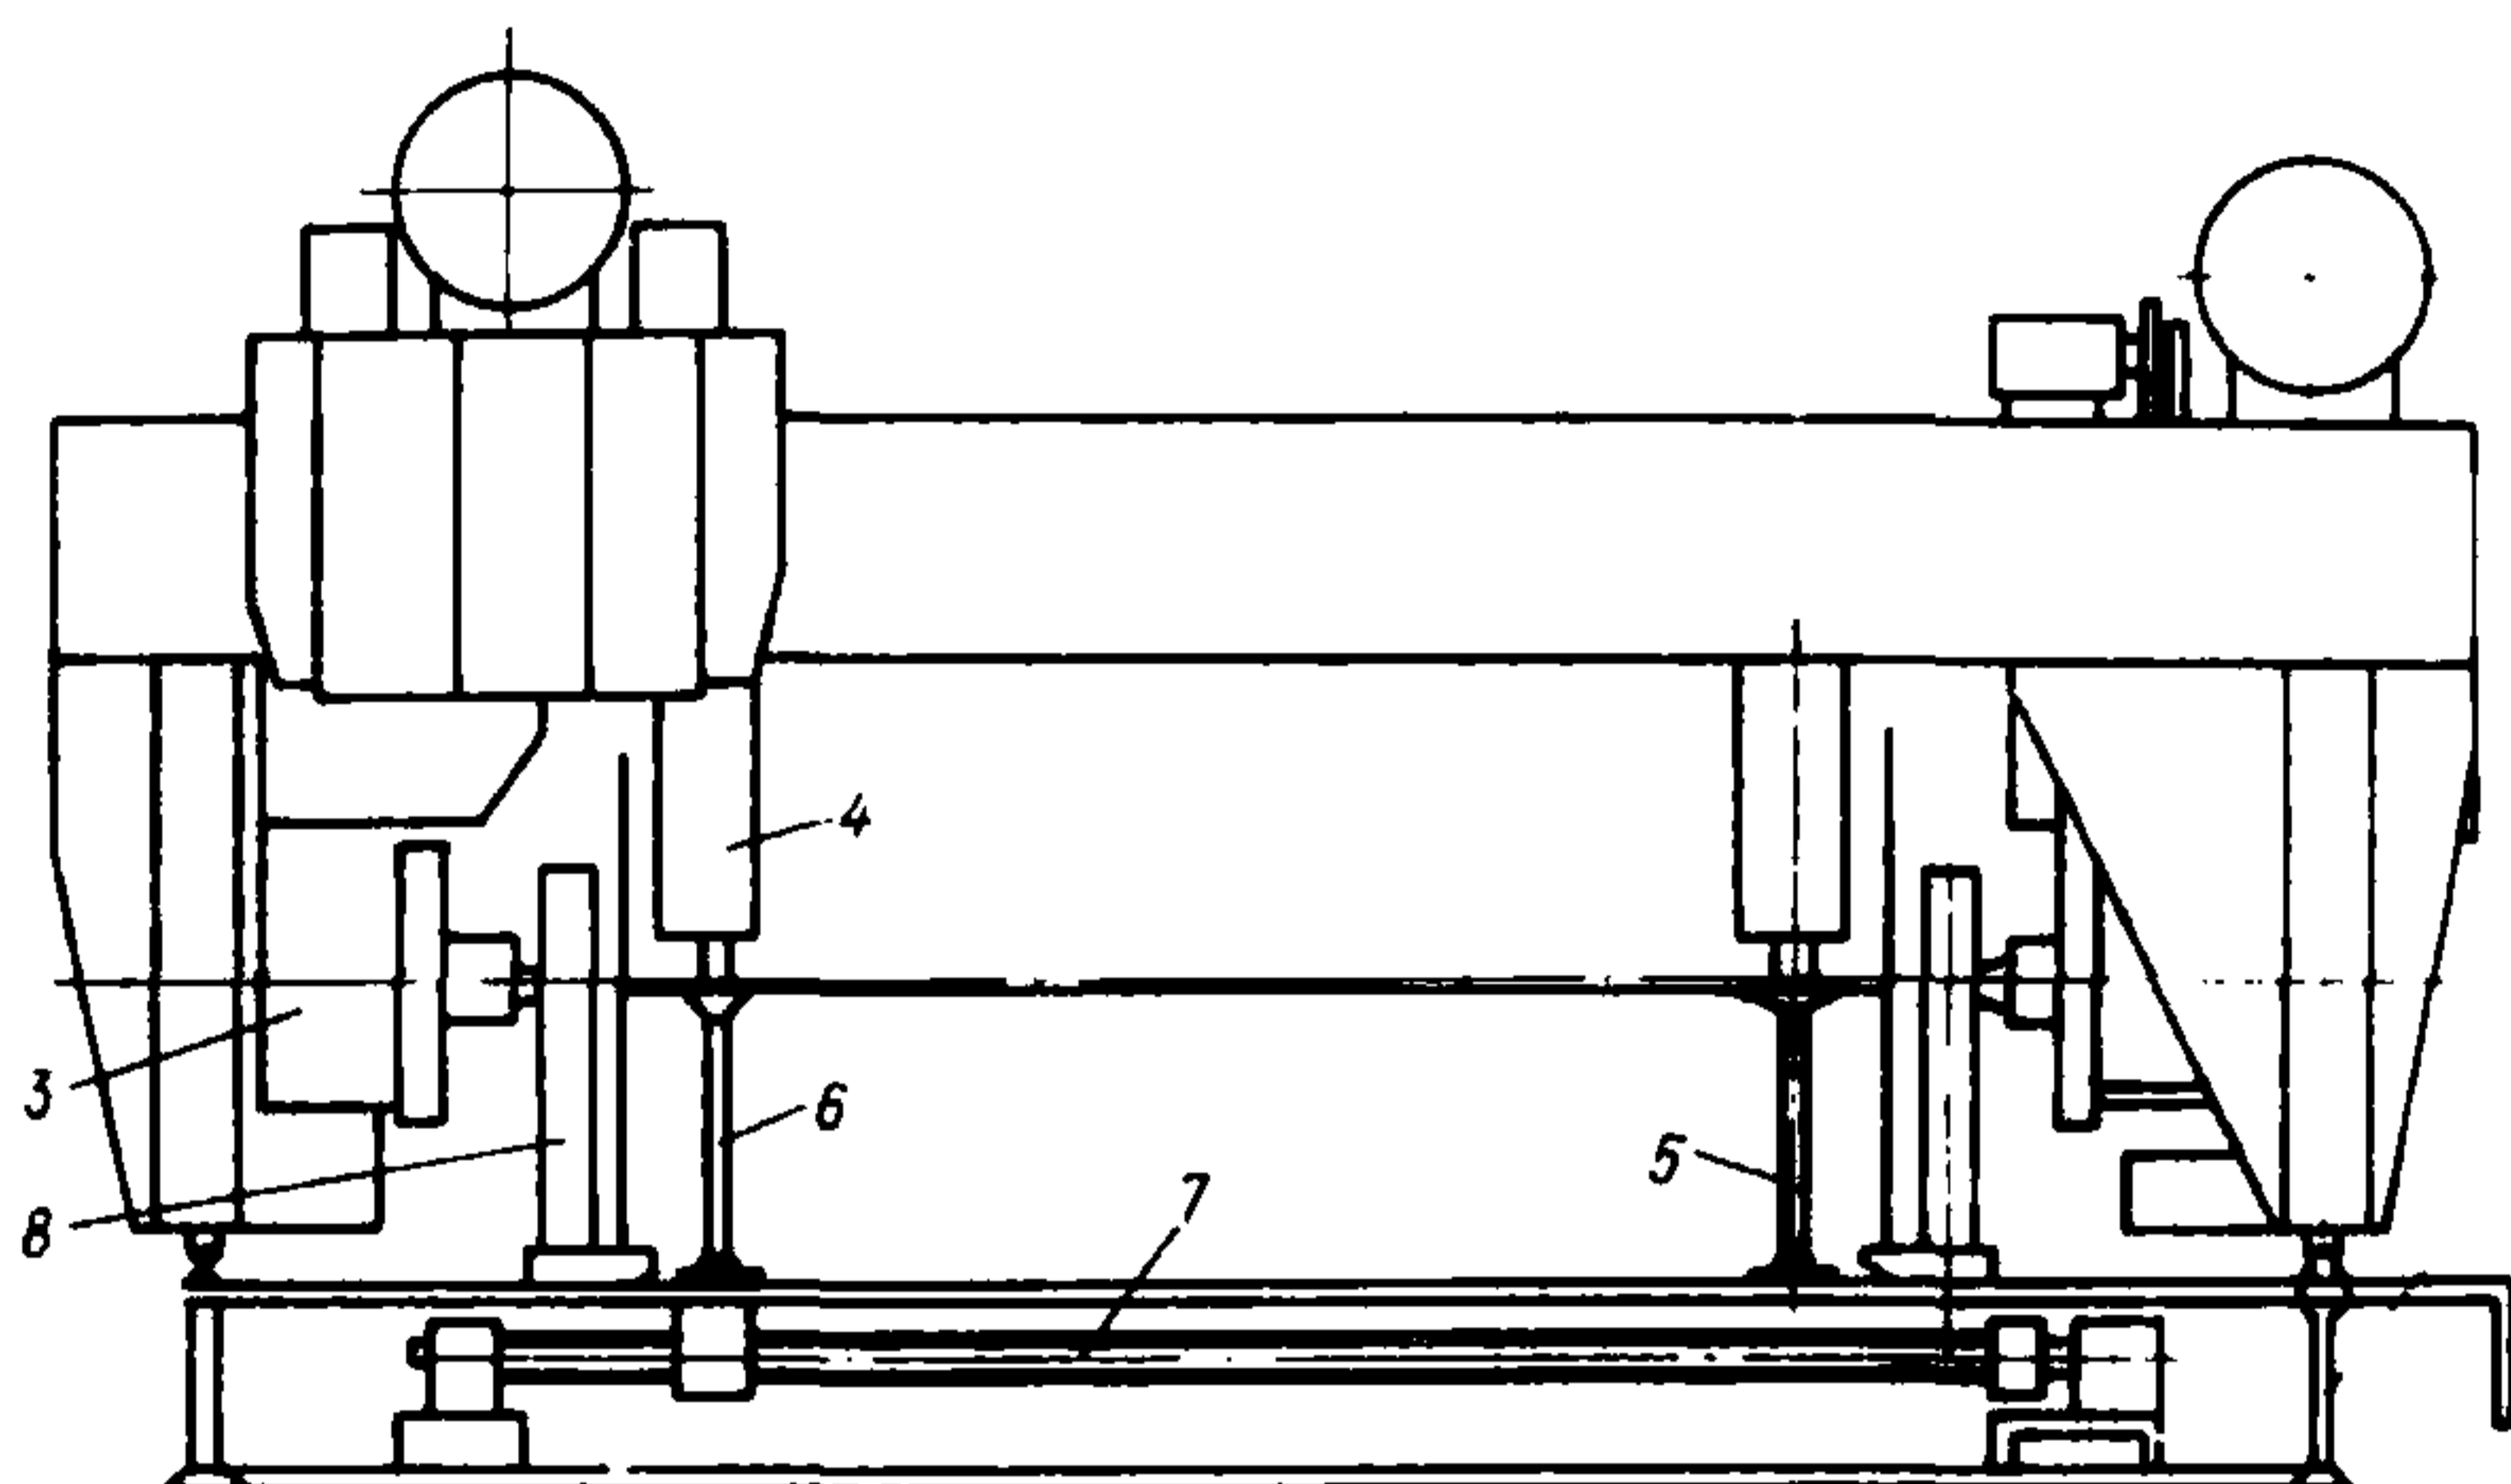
Кондуктор для сборки стержней двухтаврового сечения
